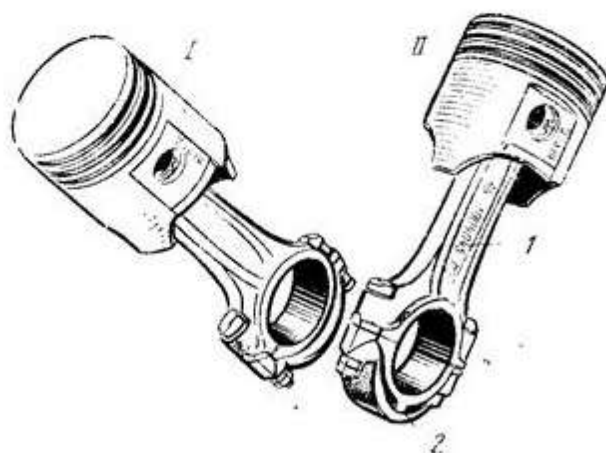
Соединение шатуна с поршнем: I — для установки в 1, 2, 3, 4 цилиндры; II — для установки в 5, 6, 7, 8 цилиндры; 1 — номер на шатуне, 2 — выточка на крышке шатуна
